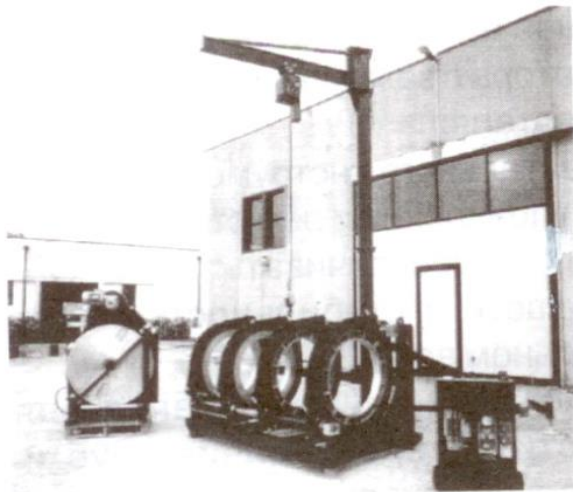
Сварочная машина «PIPEFUSE» фирмы «J.SAURON.S.A.»
